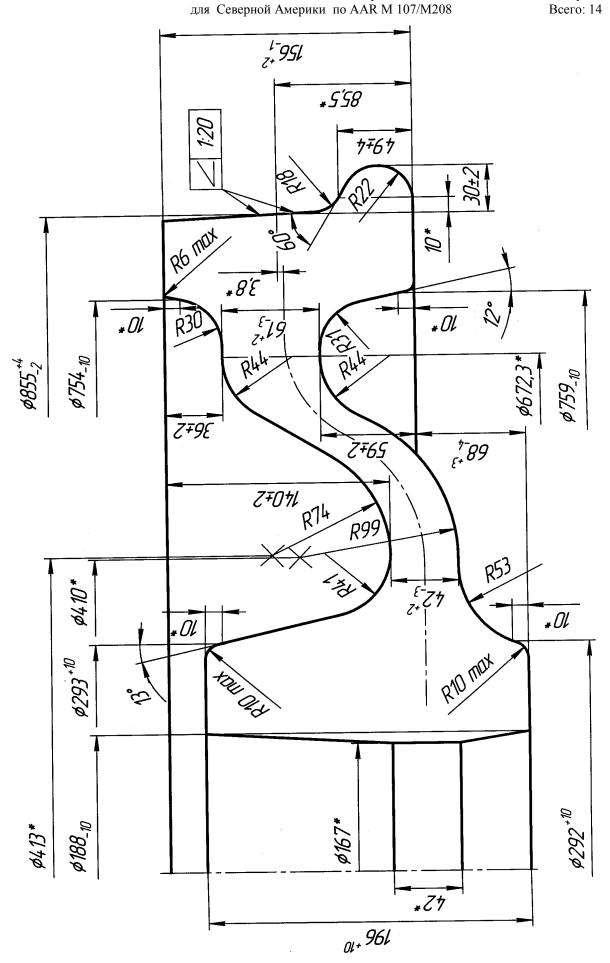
Предварительно обработанное колесо Ø 855⁺⁴-2 мм (под чистовое Ø 838мм, черт. № KP-0058-05A). Масса колеса – 448кг.
